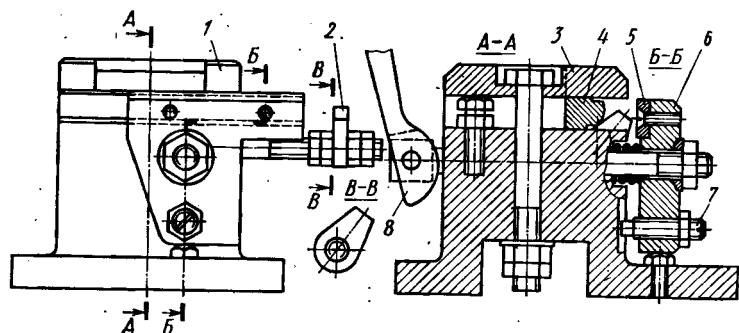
Универсальное приспособление для обработки хвостов лопаток с шириной профиля от 10 до 50 мм:
